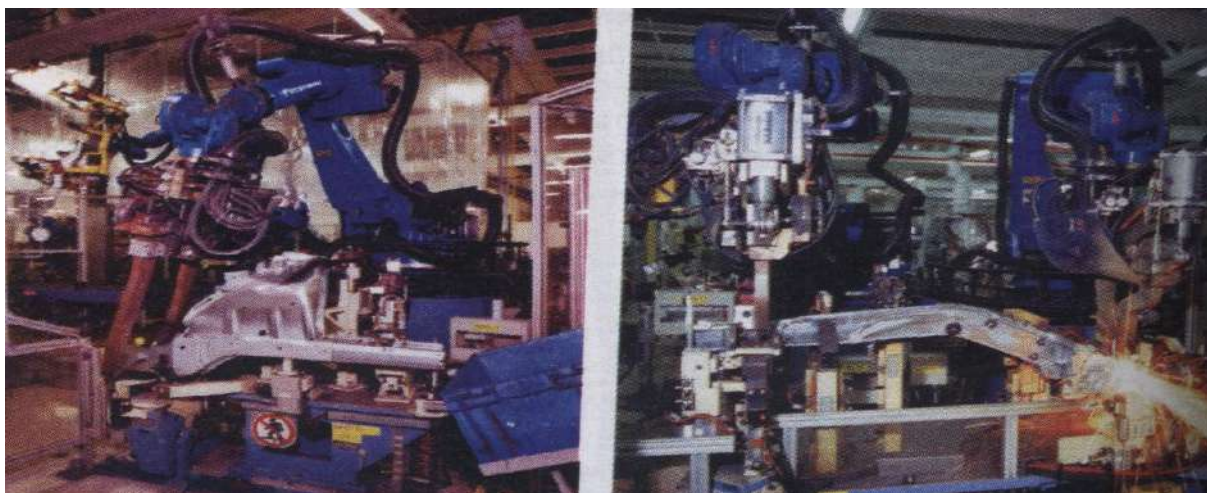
Виробничі роботи Motoman Robotics Europe AB для зварювання
